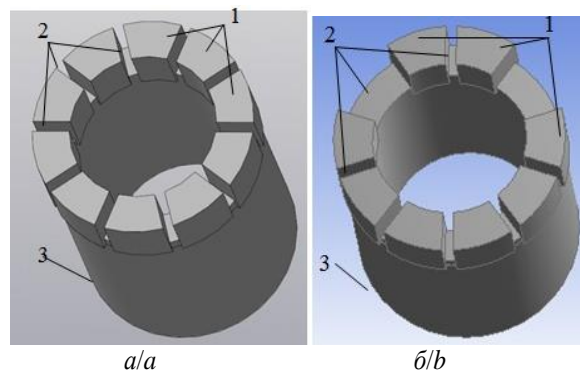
Модель исследуемой конструкции коронки: а) серийно-выпускаемая коронка КИТ типоразмера НQ; б) коронка с эксцентриситетом режущей части торца матрицы: 1 – сектор; 2 – промывочное окно; 3 – корпус
